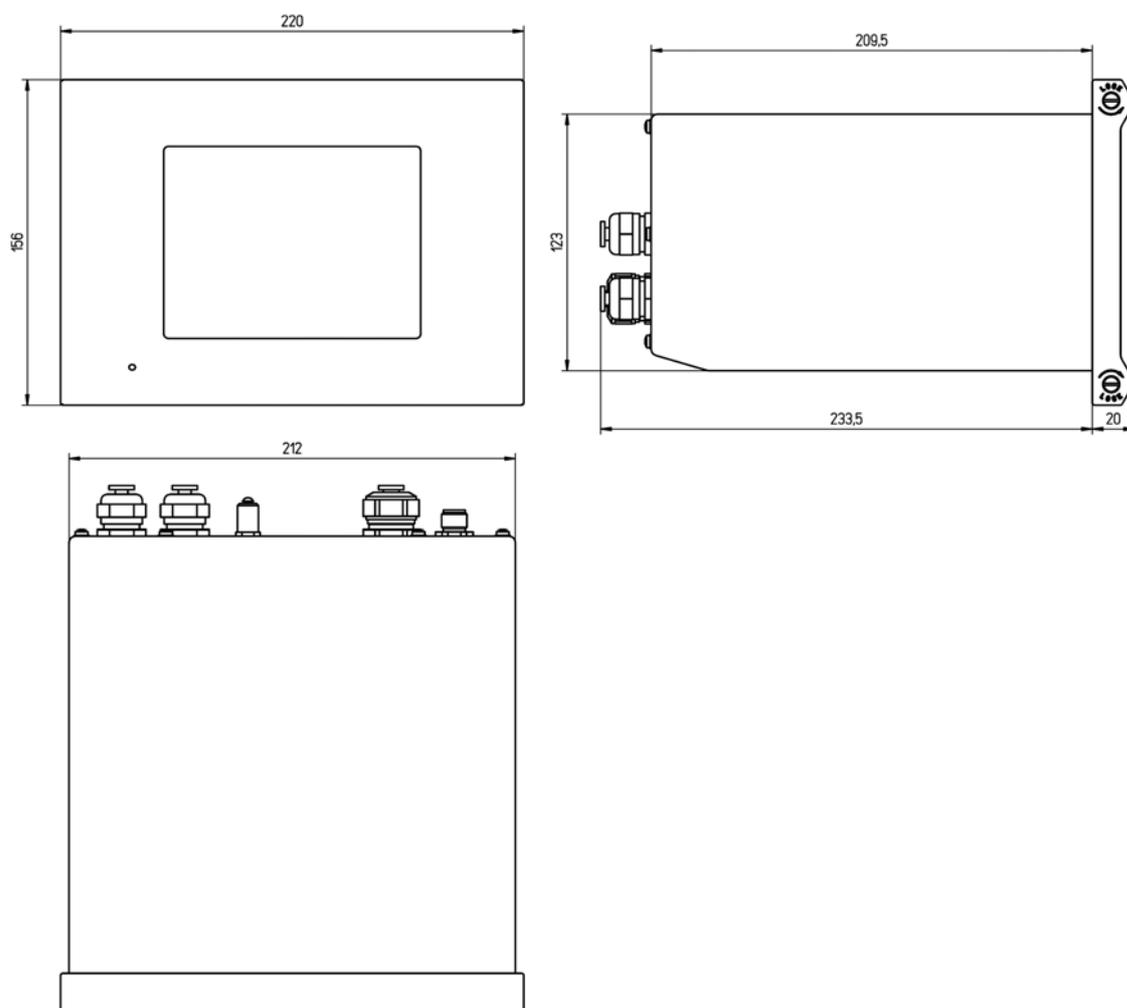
Dimensiones del instrumento: montaje en panel (en milímetros)
